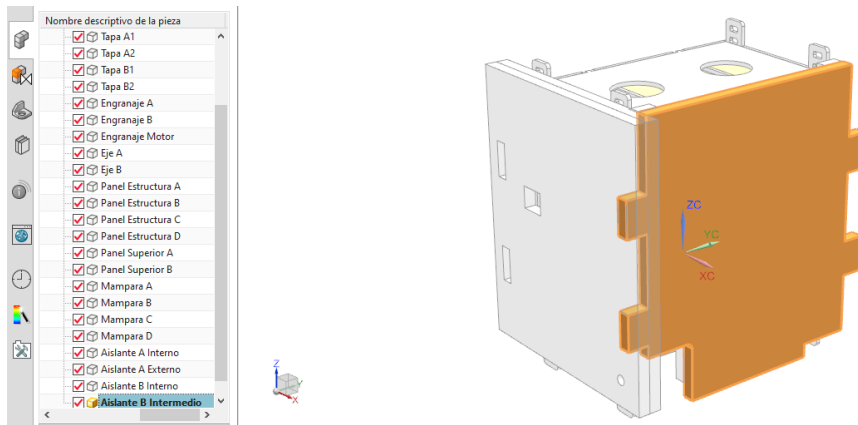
Aislante B Intermedio / Fuente: Propia
